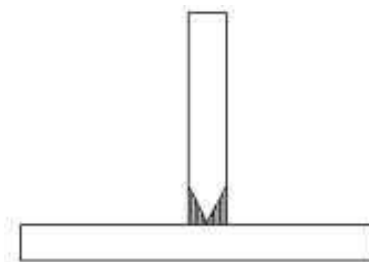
Aplicación de símbolos de soldadura
